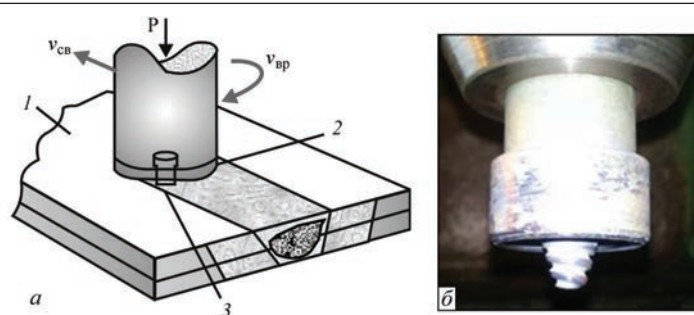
Схема процесса СТП (а) (1 — изделие; 2 — заплечник; 3 — инструмент со специальным профилем); рабочий инструмент (б)
